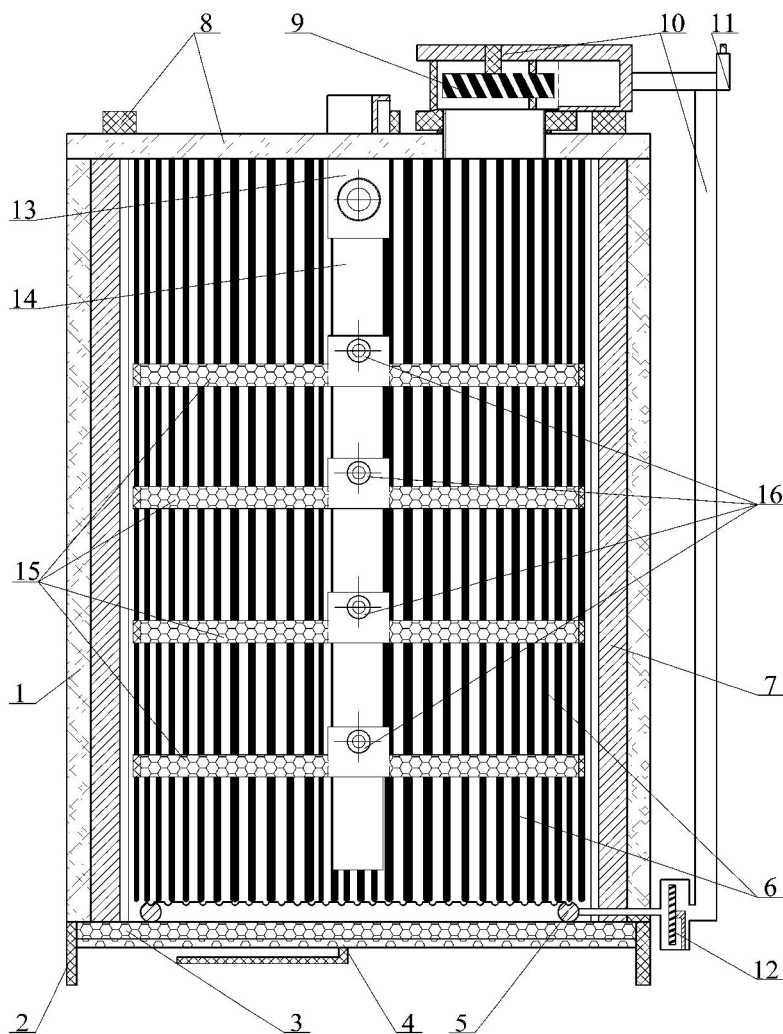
Экспериментальная ИК – сушилка: 1 – вертикальная цилиндрическая рабочая камера; 2 – стойки; 3 – распределительная решетка; 4 – регулирующая задвижка; 5 – кольцевой барботер; 6 – продольные оси рабочей камере карбоновые прямоугольные ИК-излучатели; 7 – отражающая фольга с теплоизолирующим листовым алюфомом; 8 – крышка с затяжными фиксаторами; 9 – вытяжной вентилятор; 10 – канал; 11 – регулирующая задвижка; 12 – нагнетающий вентилятор; 13 – фиксаторы; 14 – штатив; 15 – сетчатые лотки; 16 – монтажные шпильки
